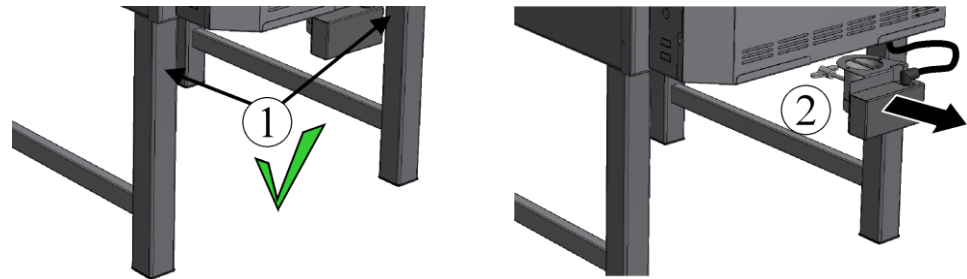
montage van de bypass-aansluiting (afbeelding vergelijkbaar)
